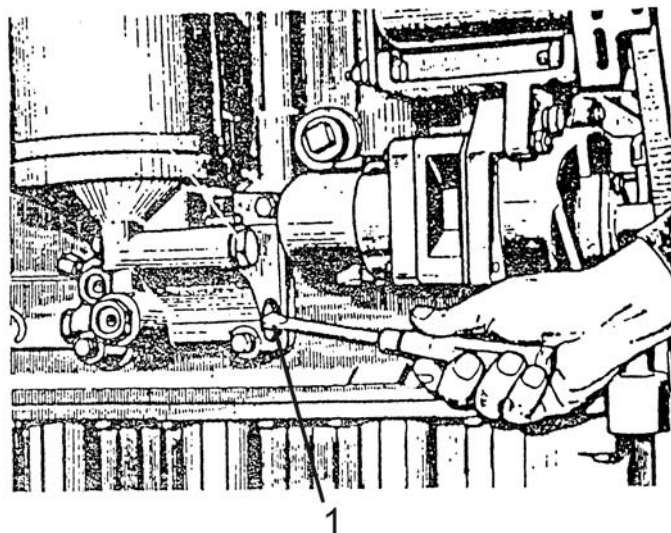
Регулировка давления в системе смазки двигателя
